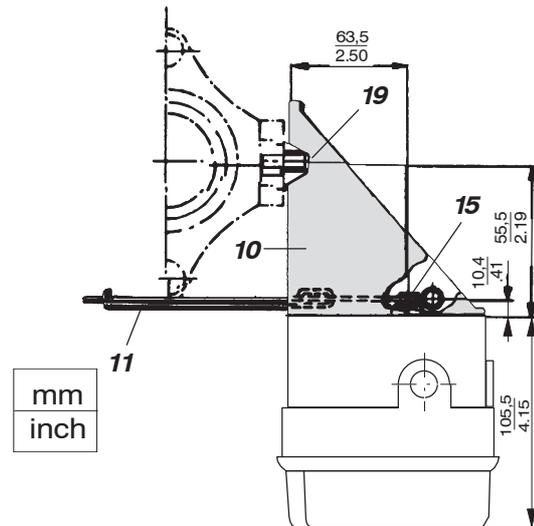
Montaje en accionamientos de membrana con linterna de fundición según DIN IEC 534-6 (montaje a la derecha), código G
